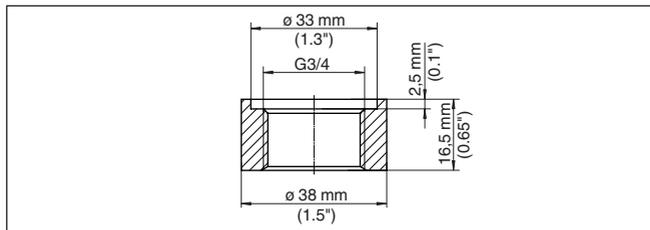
Dimensiones racor para soldar rosca G $\frac{3}{4}$ (DIN 3852-X)
